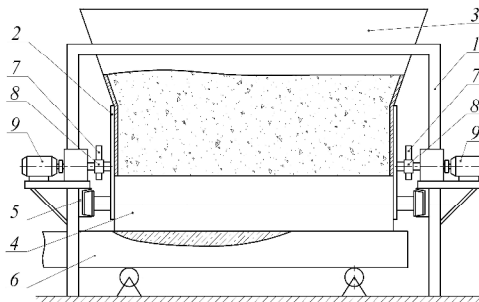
Роликовая формовочная установка с кулачковым приводным механизмом
